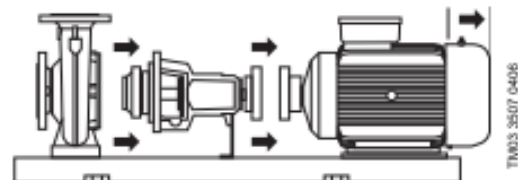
Vista esquemática del principio de desmontaje para bombas NK
